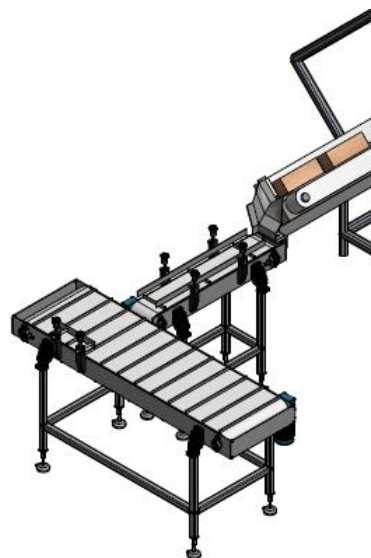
Disposición de MD junto a Riel-Guía y BTMP1.
